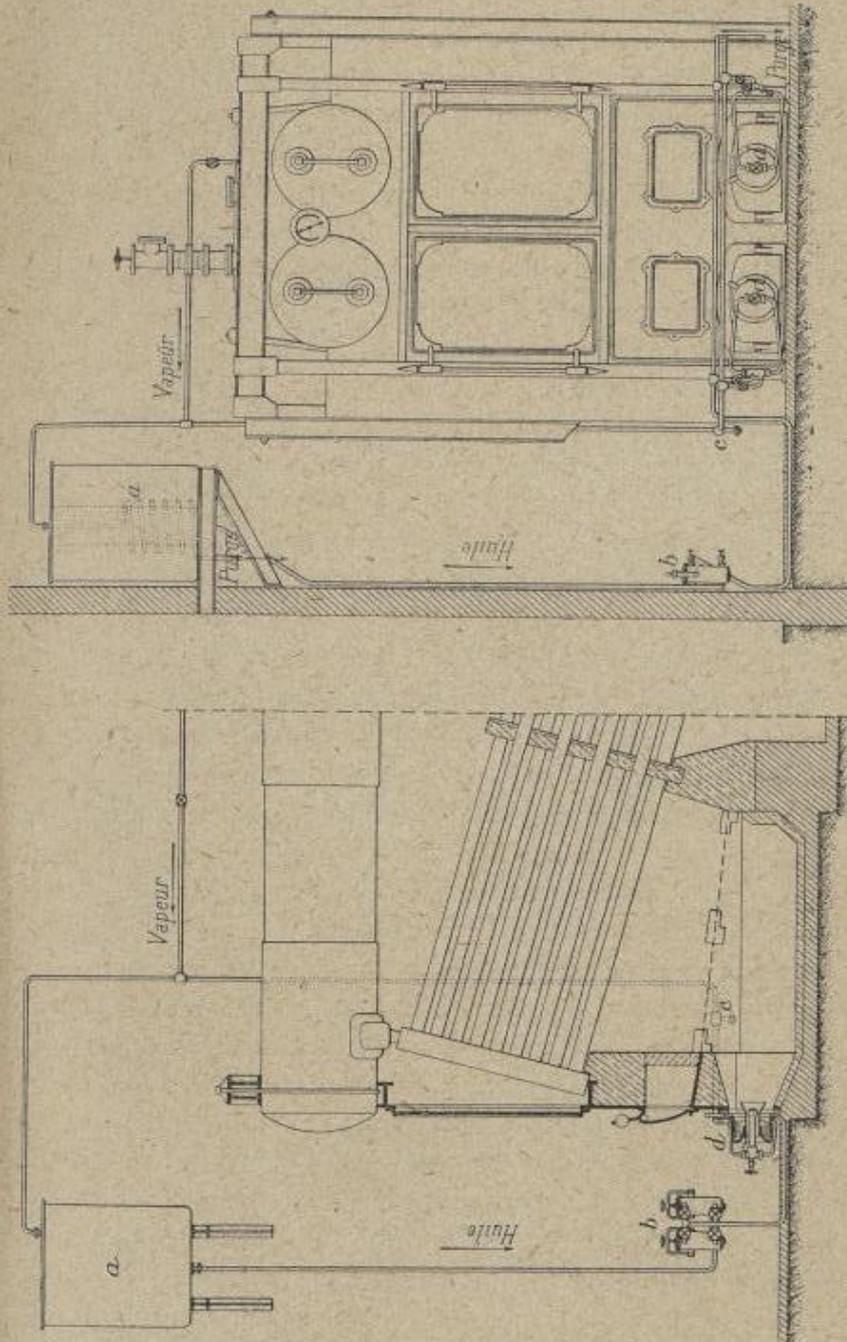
Brûleur Gènevet, sous une chaudière Babcock et Wilcox.
